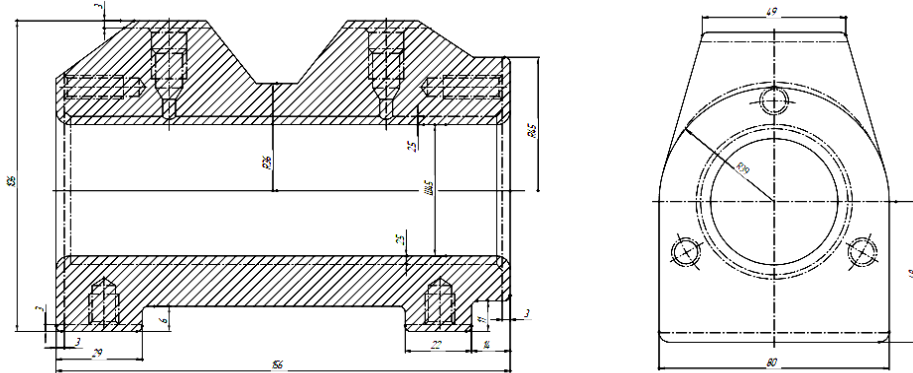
Загальний вигляд зготовки «Корпус гідропідсилювача ПЕА 01.105»
